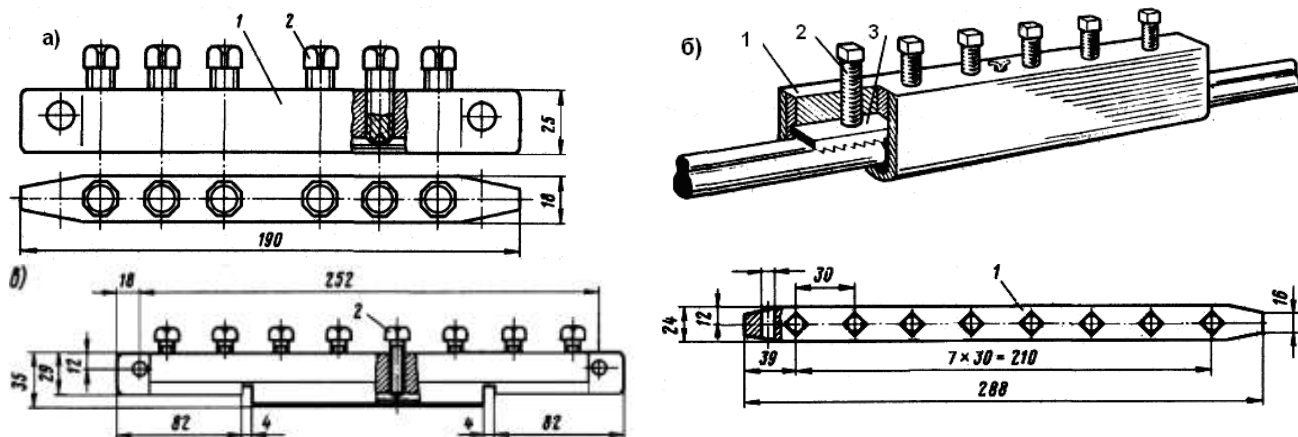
Затискачі стикові: а - тролейбусний ЗС; б - типу обхвату для сталевалюмінієвого проводу; в - для сталевалюмінієвого проводу з роздільним захопленням сталеві і алюмінієвої частин; 1 - корпус; 2 - болт спеціальний; 3 - зубчаста рейка
